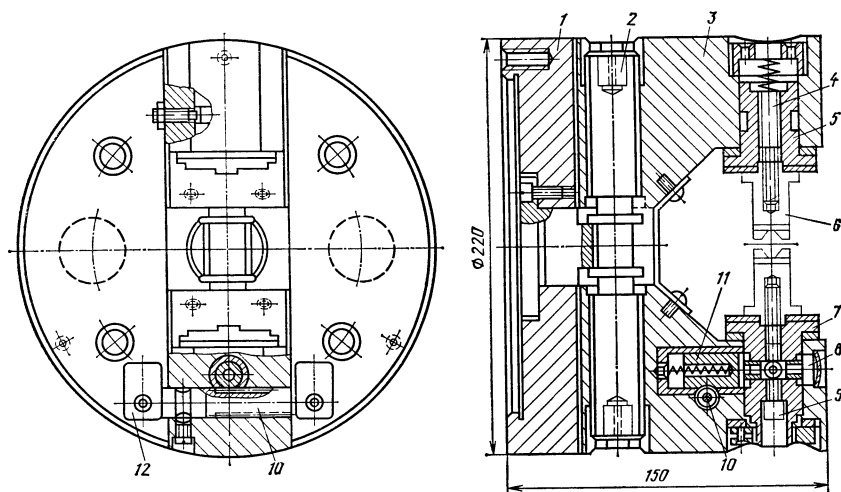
Специализированный наладочный двухкулачковый патрон для позиционной обработки деталей арматуры
